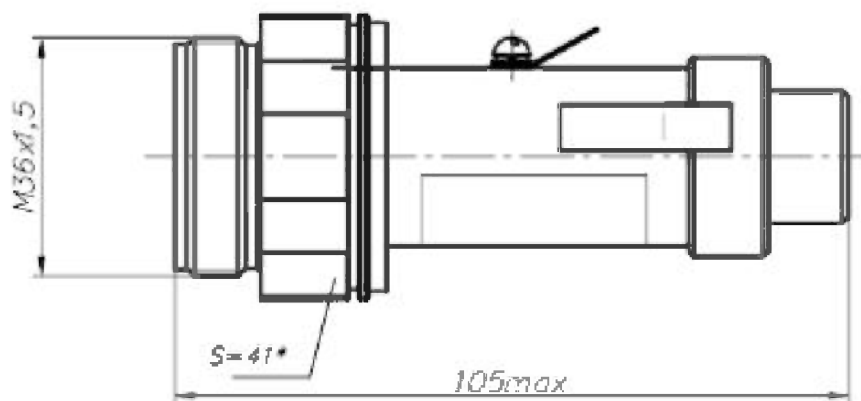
Габаритный чертёж преобразователей избыточного давления, давления-разрежения (с кодом присоединительного размера 1, 2, 6–8, С–F, К, L по таблице А.8 и кодом конструктивного исполнения К00 по таблице А.14), избыточного, абсолютного давления (с кодом присоединительного размера 1, 2, 6–8, С–F, К, L по таблице А.8 и кодом конструктивного исполнения К04 по таблице А.14)
